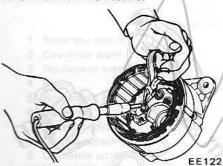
Dépose de la soudure de liaison entre le bobinage de stator et les diodes
